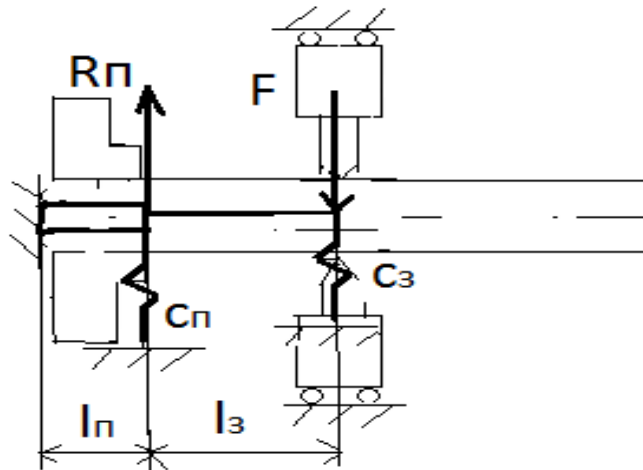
Розрахункова схеми пружних систем патрона із заготовкою і дворізного пристрою
